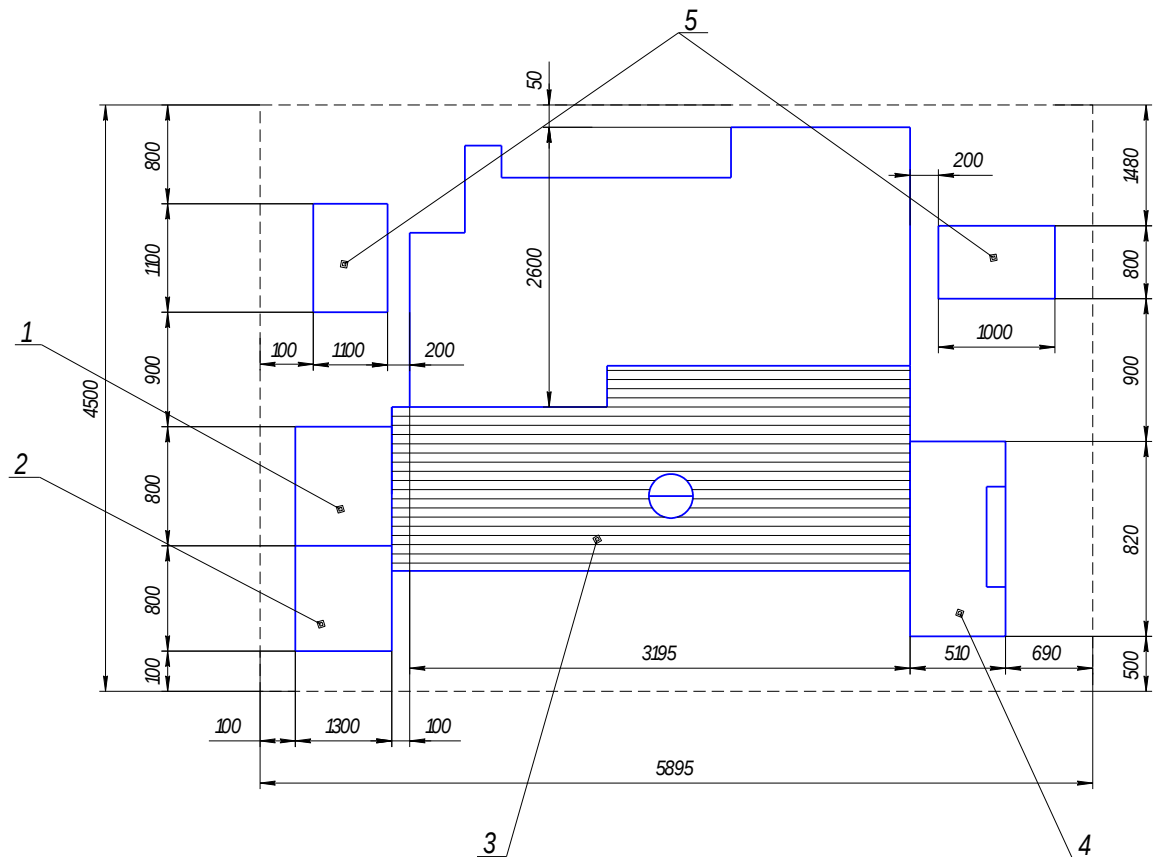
План робочої зони оператора токарного вертикального двошпиндельного верстата з ЧПК: 1 – приймальний стіл; 2 – тара; 3 – решітка для ніг; 4 – інструментальна шафа для двохзмінної роботи; 5 – стелаж для пристосувань
